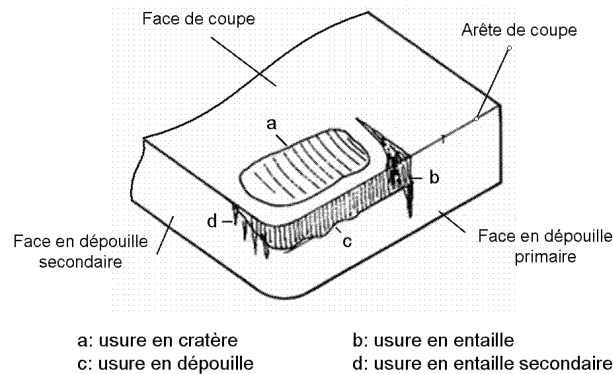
Principales formes d'usure d'un outil de coupe [LERO 93]
